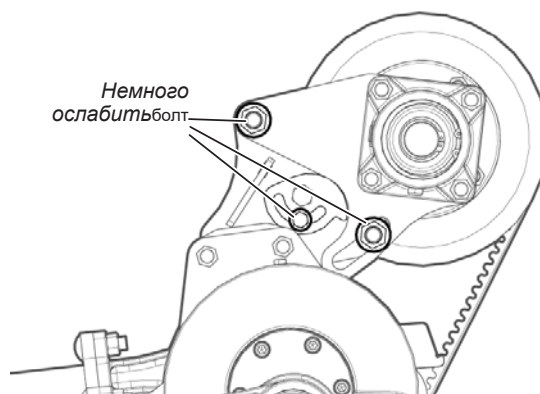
Натяжение ремня ножей: ослабление стопорной гайки и болта.
